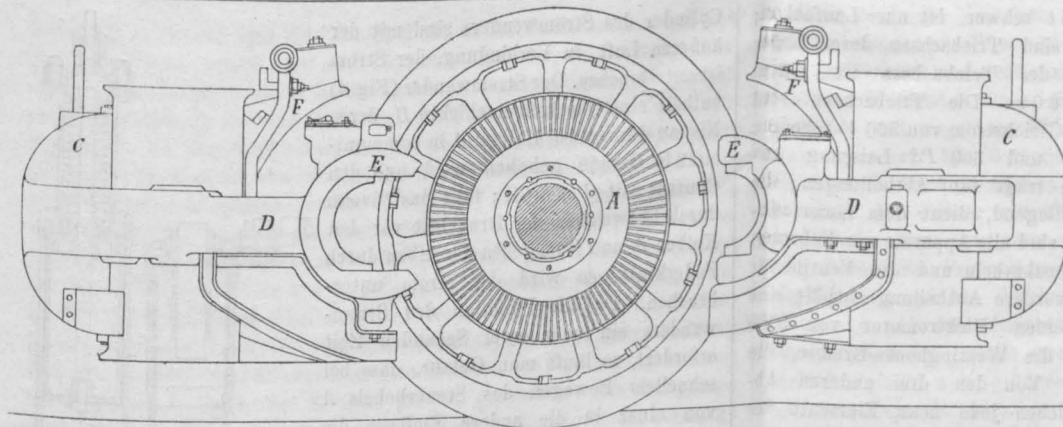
Seitenansicht des Motors mit auseinander geschobenen Magneten.
